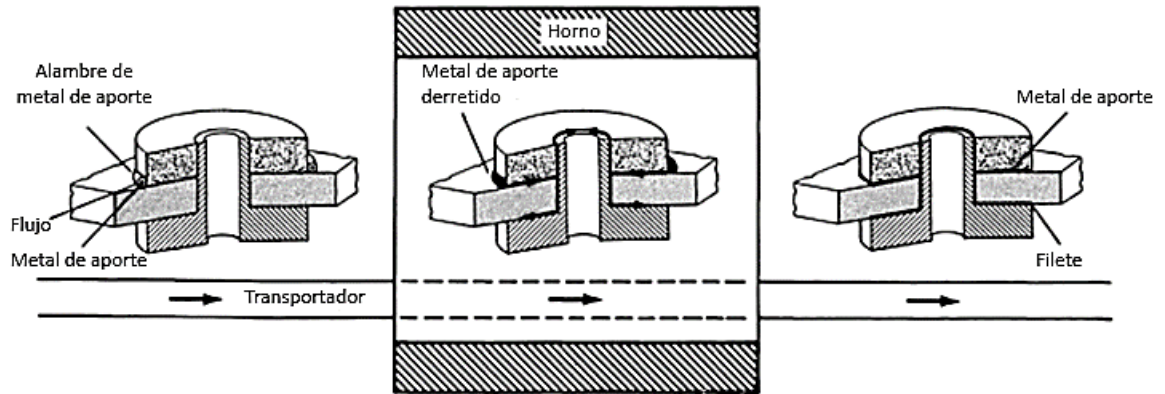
6 Esquema de operación de la soldadura brazing en horno. (7)
